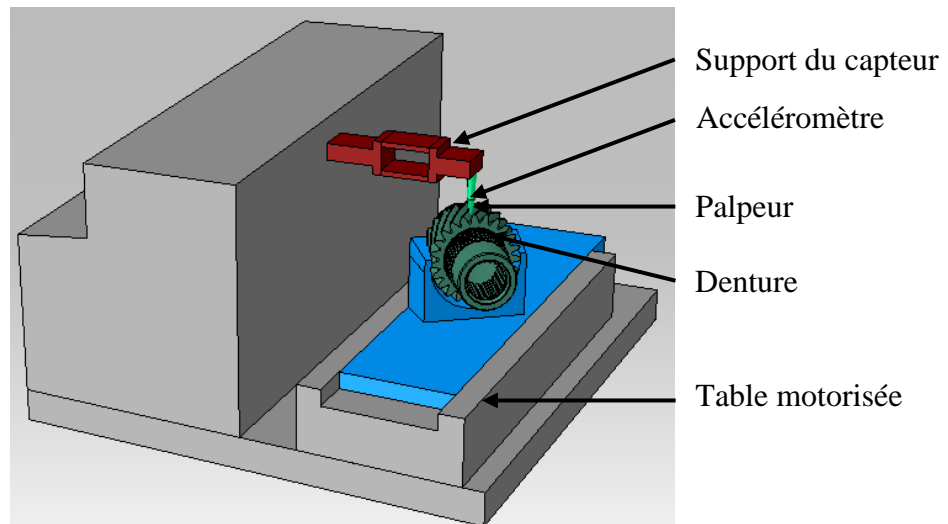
Schéma du dispositif de mesure de bruit de frottement pour les flancs de denture. La partie mouvante est en bleu.
